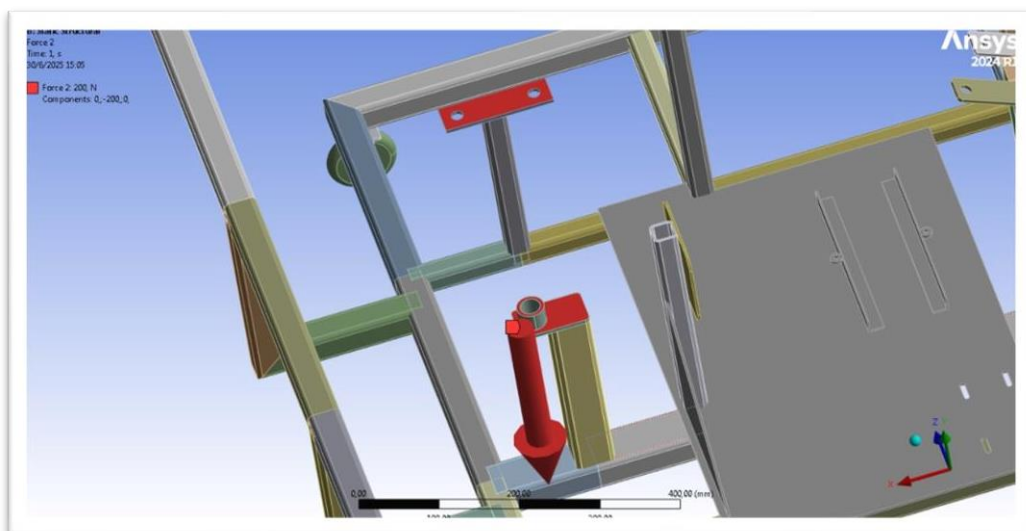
Fuerza de la columna de dirección y la articulación de la columna
